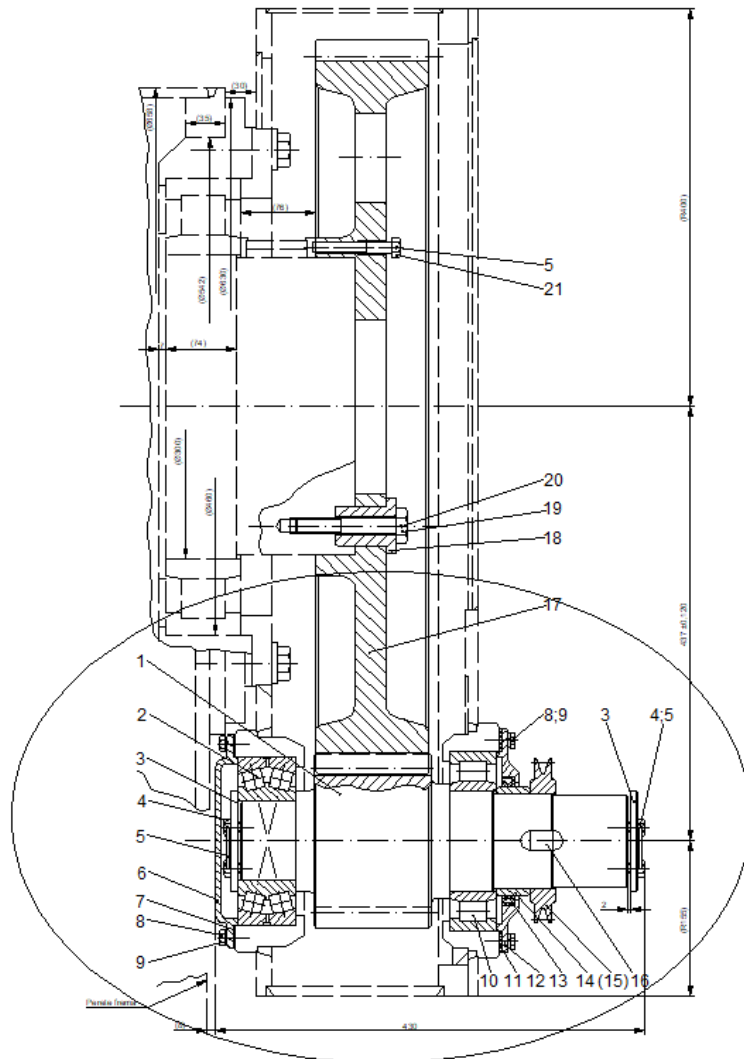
b. Sectiune verticala prin angrenaj mecanism motor – Coroana dintata
